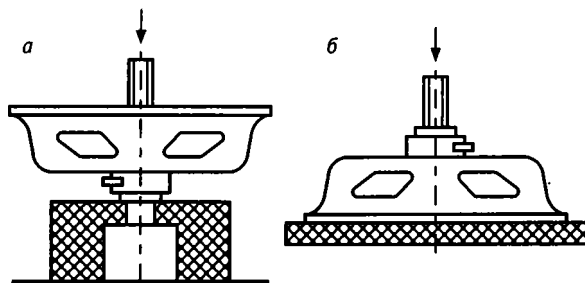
Установка подшипникового щита электродвигателя при выбивании вкладыша:
